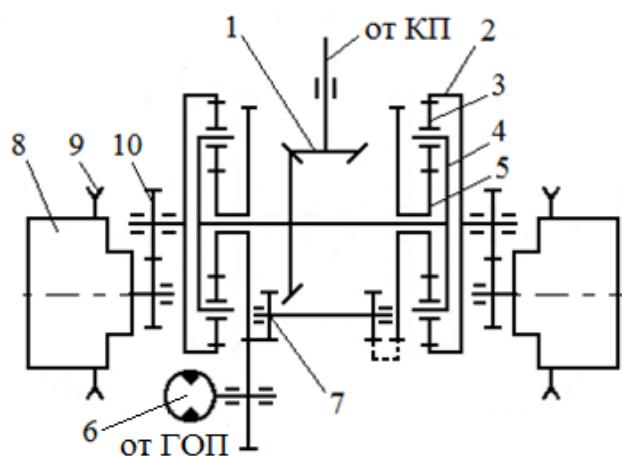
Схема бесступенчатого дифференциального механизма поворота: 1 – центральная передача; 2 - эпицикллическое колесо; 3 – сателлит; 4 – водило; 5 – солнечная шестерня 6 – гидромотор ГОП; 7 – привода поворота; 8 – бортовой редуктор; 9 – ведущее колесо; 10 – бортовая передача
